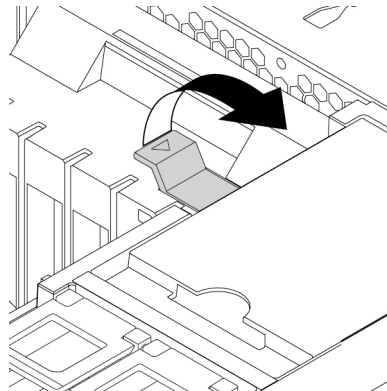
Abrindo a trava no conjunto do ventilador frontal
